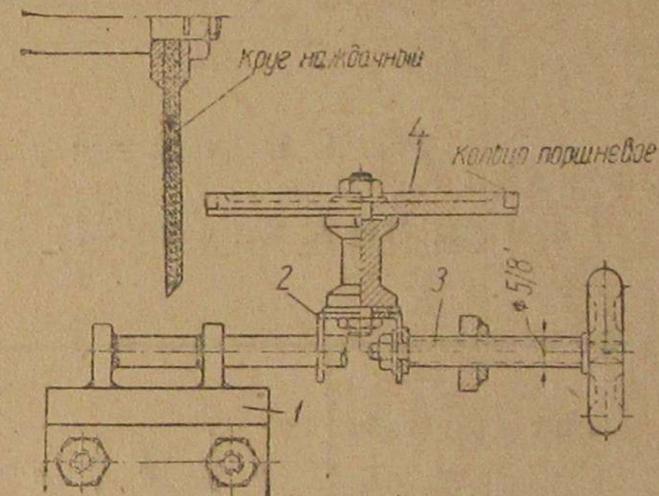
Установка приспособления для шлифовки поршневых колец у наждачного круга:
